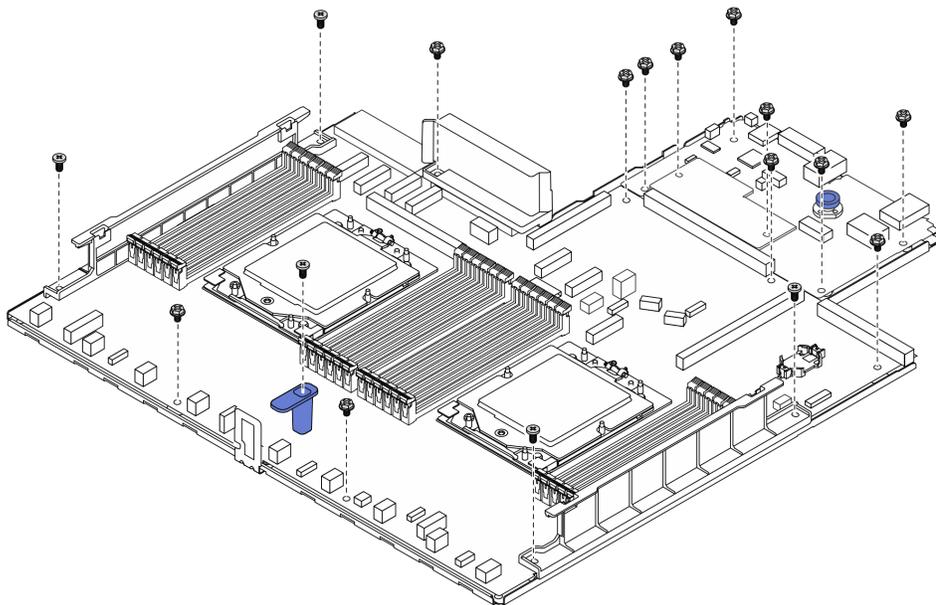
Entfernen der Schrauben von der Prozessorplatine
